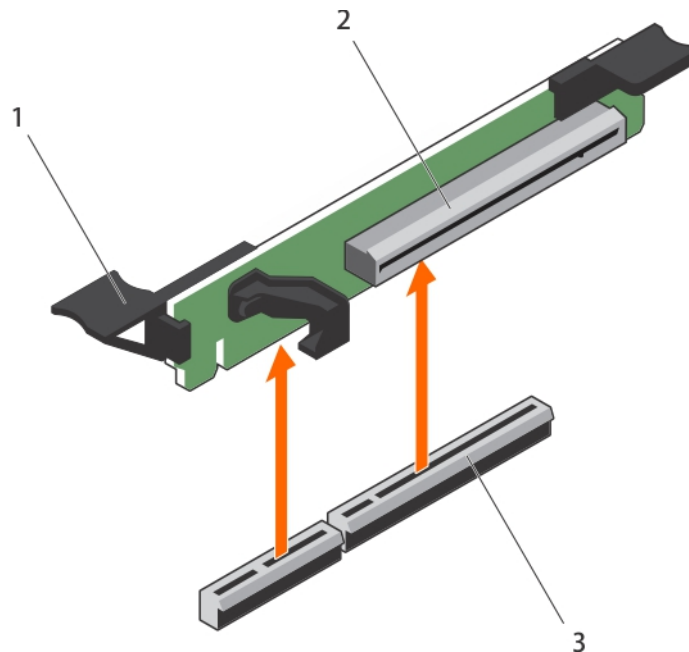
Retrait de la carte de montage pour carte d'extension 3
